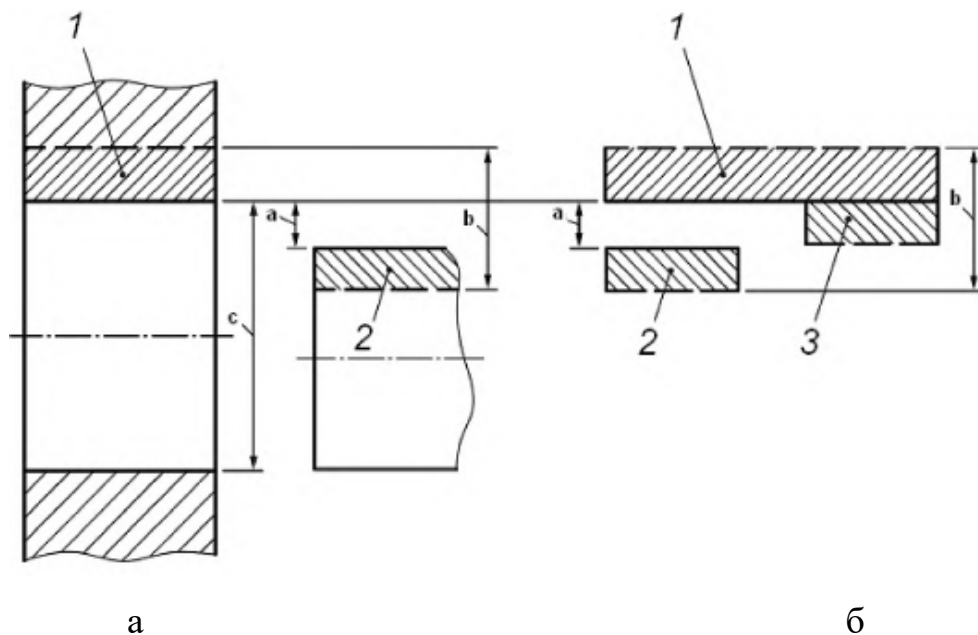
Графическое представление посадки с зазором в системе отверстия: подробное (а) и схематическое (б); 1 – интервал допуска основного отверстия; 2 – интервал допуска вала с гарантированным зазором; 3 – интервал допуска вала с нулевым минимальным зазором; а – наименьший зазор; б – наибольший зазор; с – номинальный размер соединения
